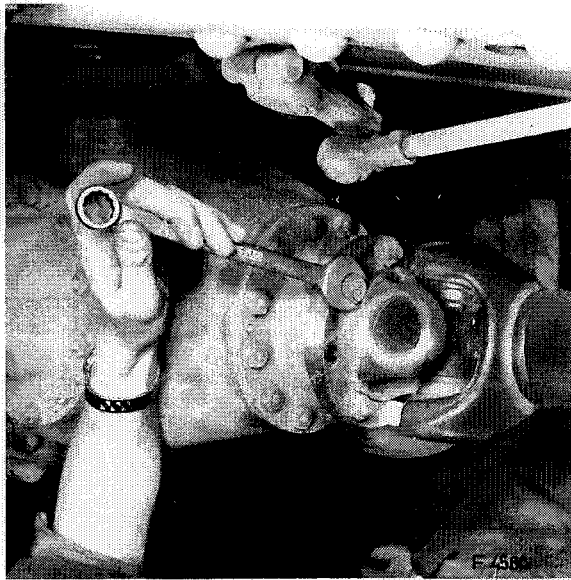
Lösen der Befestigungsschrauben am Flansch einer Rohrwelle des Längstriebes
